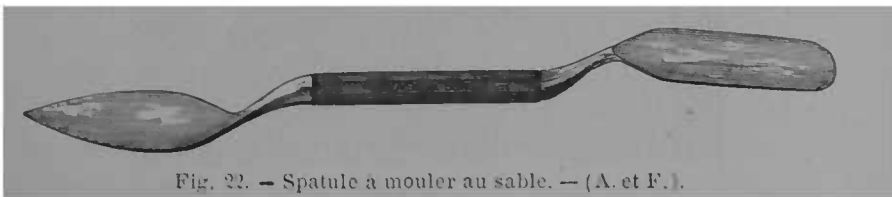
Spatule à mouler au sable. — (A. et F.).
